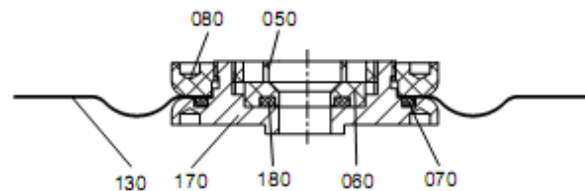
Схема сборки инжекторов 0,5- 4,0 кг/ч
